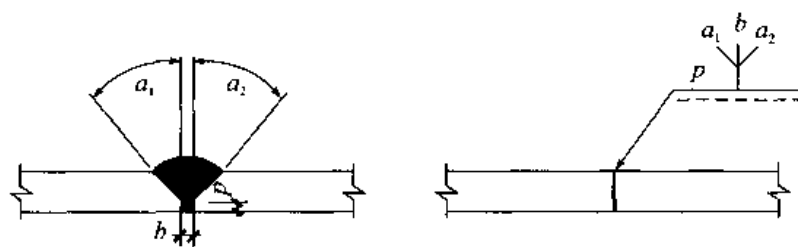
单面不对称坡口焊缝的标注方法
